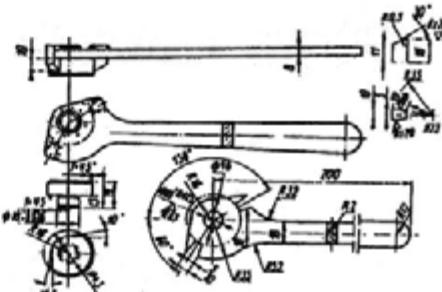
Ключ для подтяжки регулировочных гаек подшипников коробки дифференциала:
